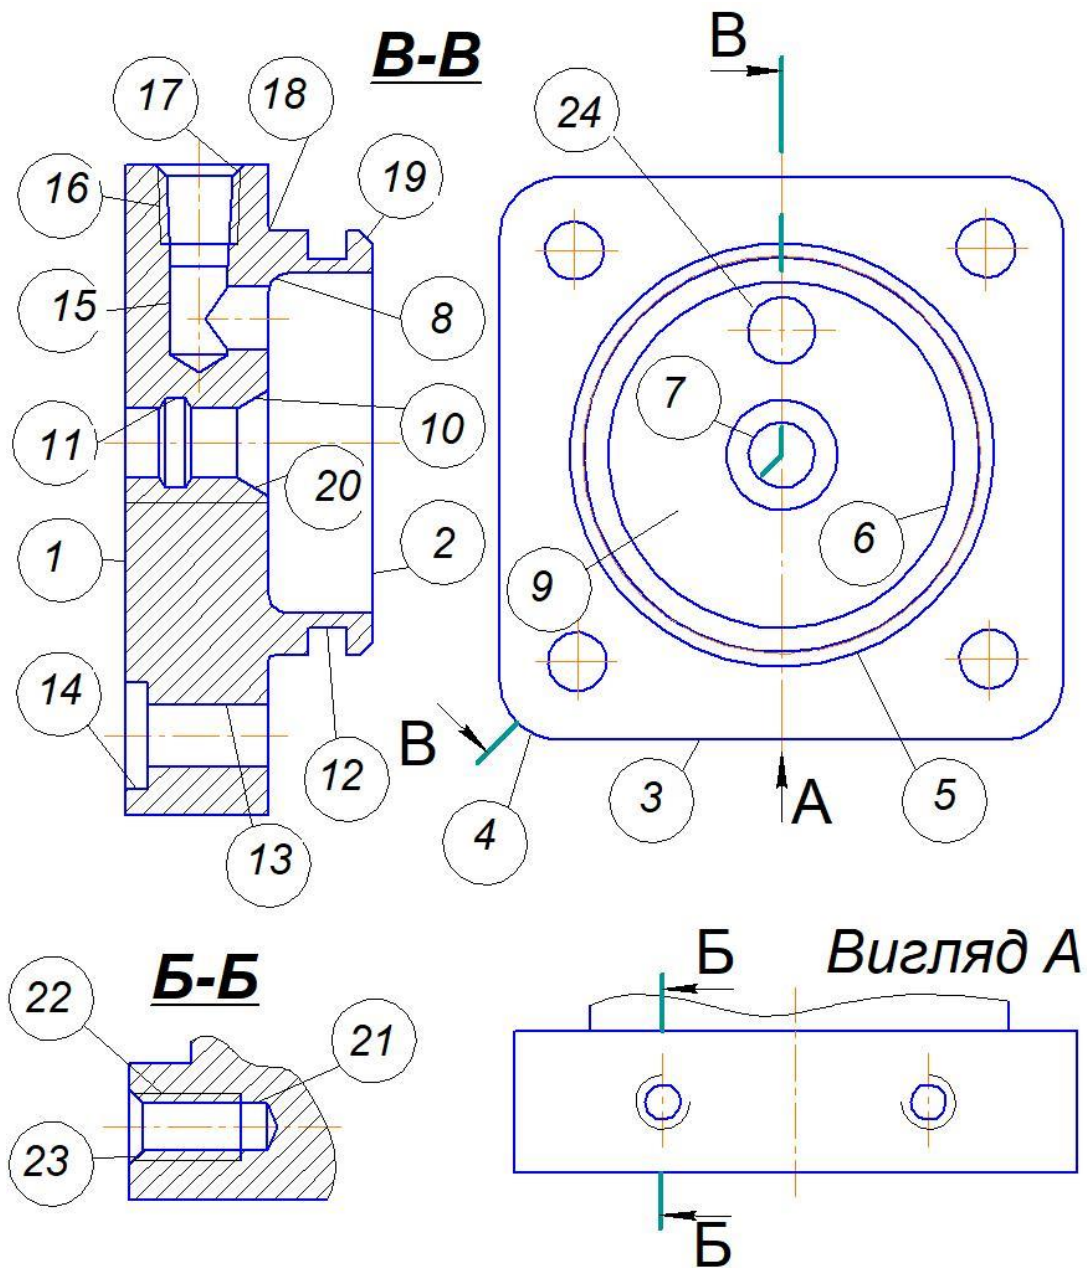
Ескіз деталі «Кришка KB2132-22-102» з номерами поверхонь
